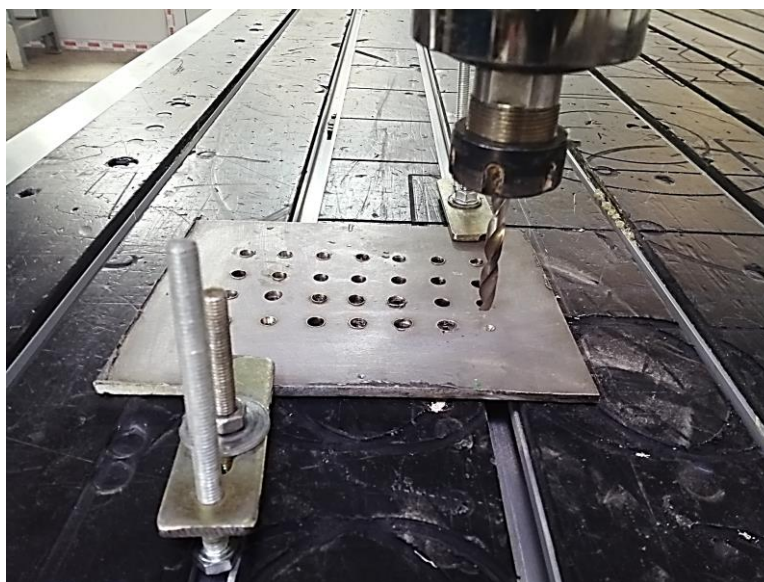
Испытания сверла на фрезерном станке с ЧПУ PHILICAM 2030
